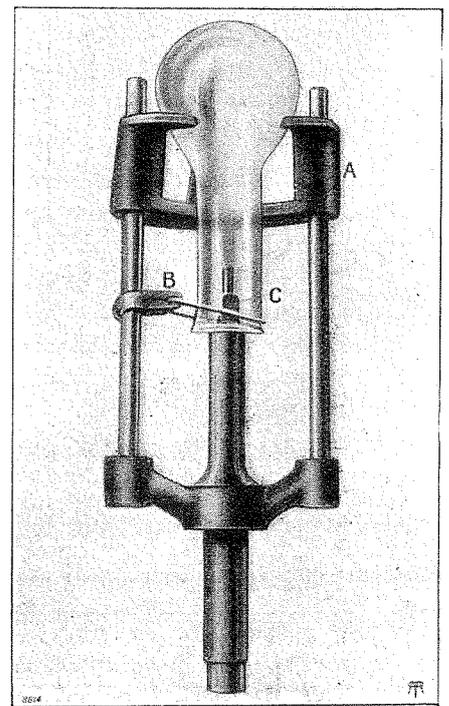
Vue d'un type de support (a, fig. 15) pour machine à fermer.
